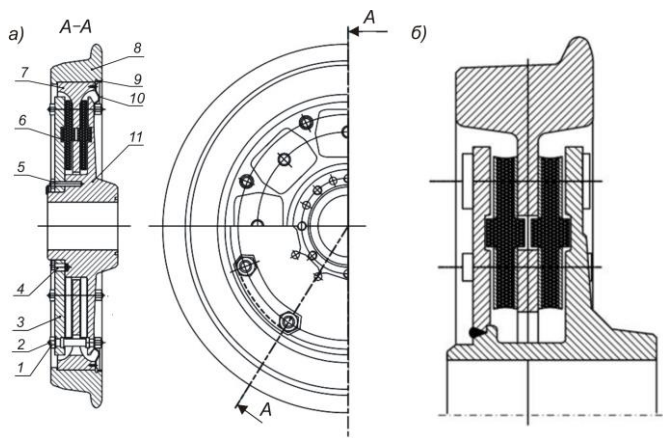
Конструкции колес с двумя резиновыми кольцами:
